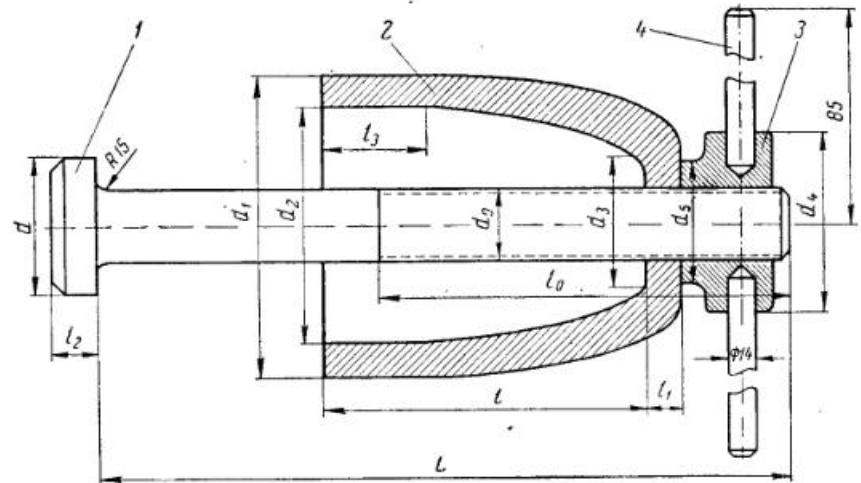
Приспособление для выпрессовки направляющих втулок клапанов:
